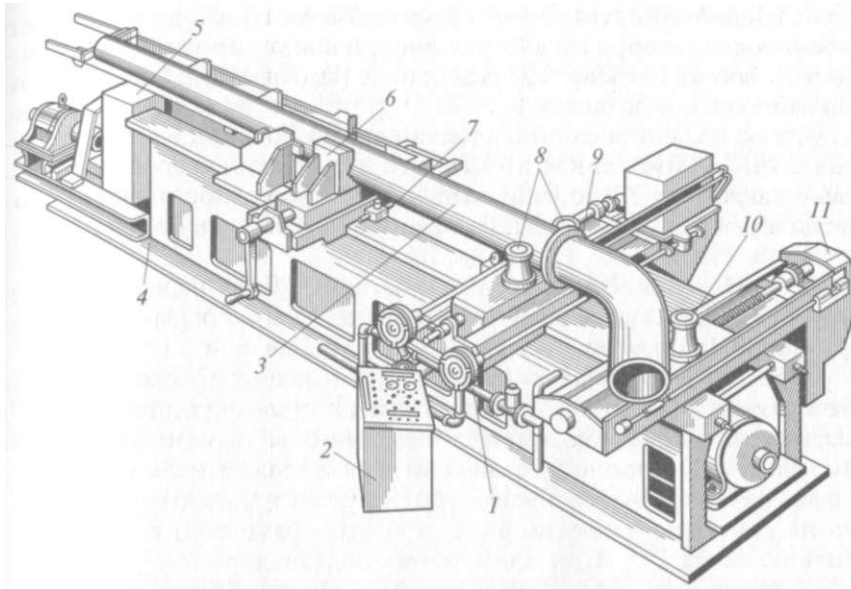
Станок ТГС-325 для гибки труб с нагревом ТВЧ:
